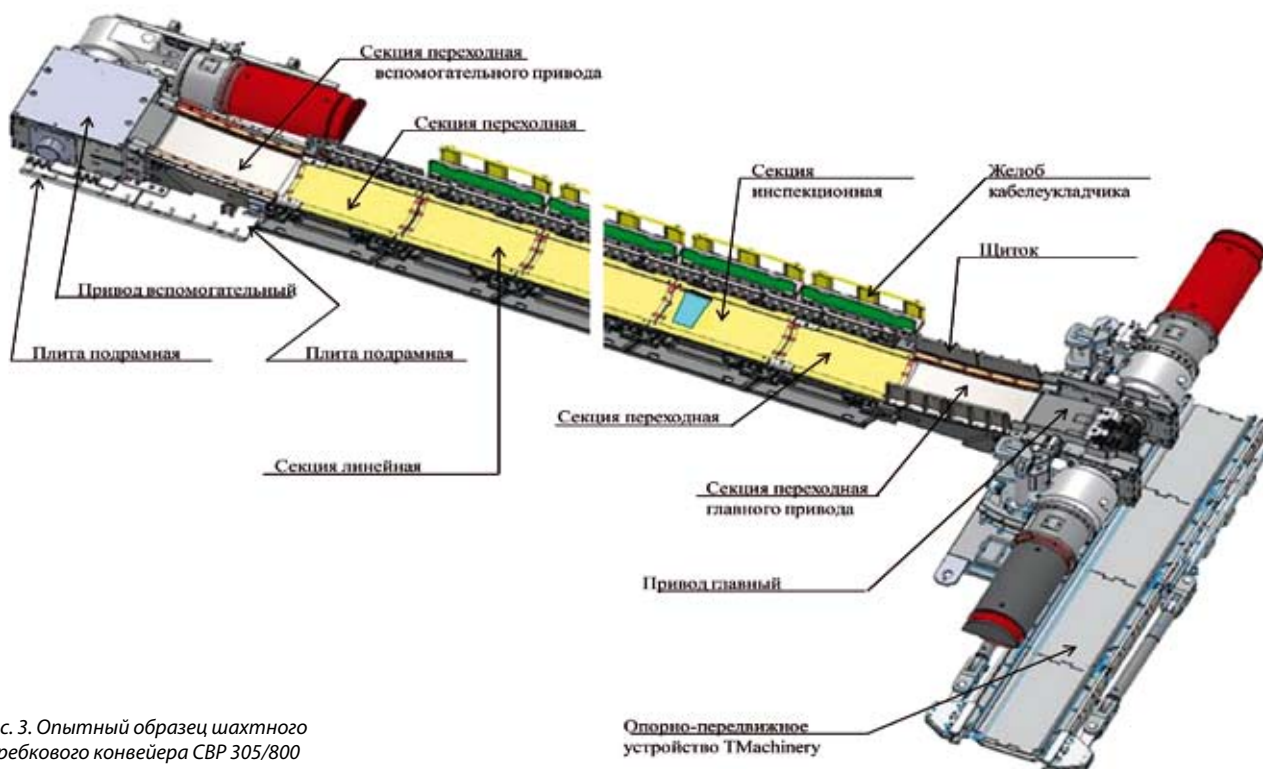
Опытный образец шахтного скребкового конвейера СВР 305/800
